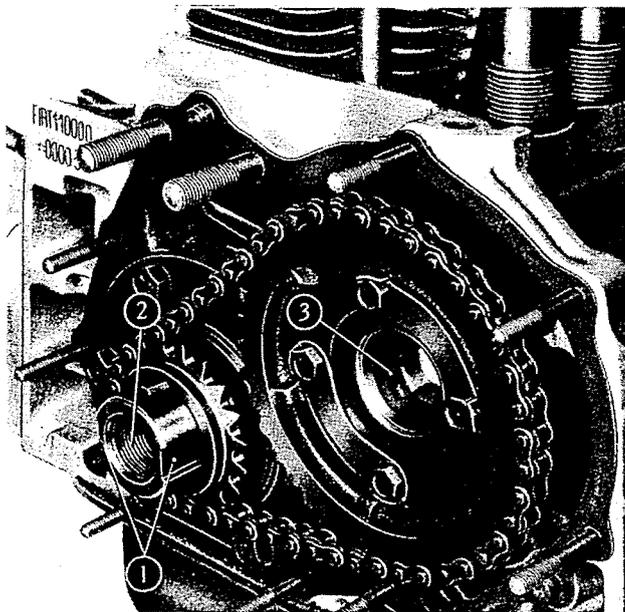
Kurbelwellenzapfen und Steuerräder.
